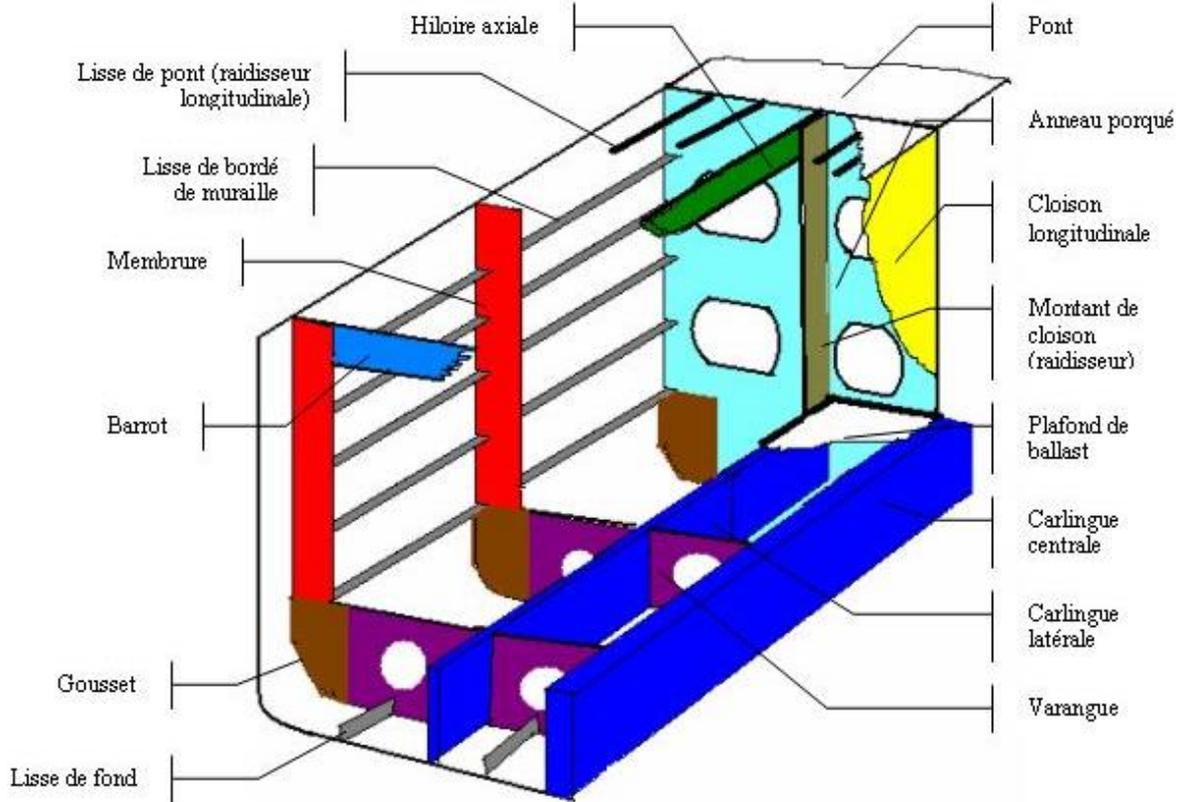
Vue en 3D de la structure d'un navire avec diffèrent liaisons de pont de muraille et de fond.
